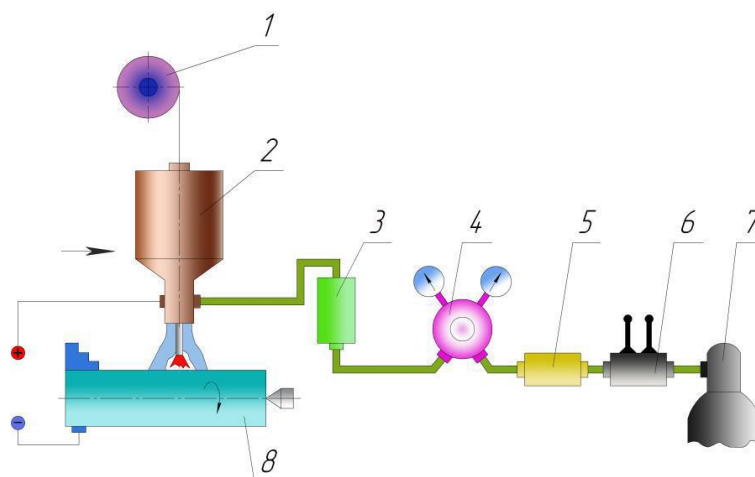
Схема выполнения ручной дуговой наплавки
